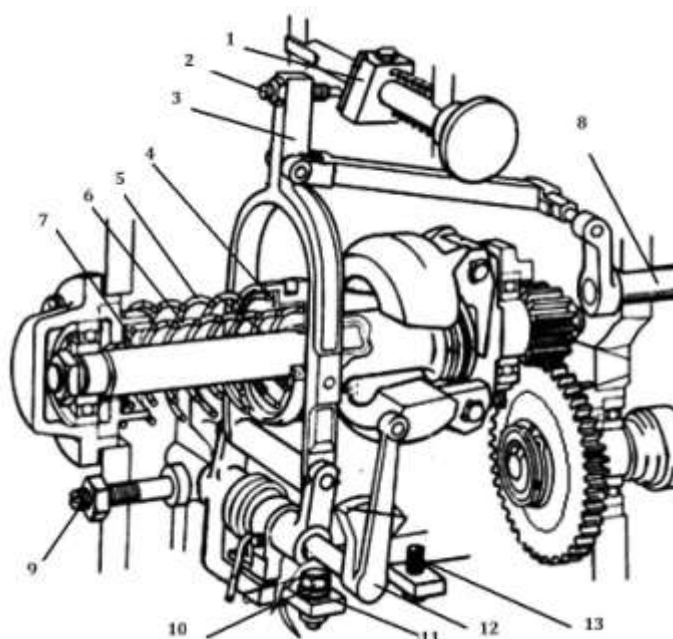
Регулятор ТНВД серии ТН: 1 - призма; 2 - болт номинала; регулировочные шайбы; 3 - основной рычаг; 4, 7, 11 - регулировочная шайба; 5, 6 - пружина регулятора; 8 - рейка топливного насоса; 9 - болт-ограничитель; 10 - болт максимального скоростного режима; 12 - рычаг управления регулятором; 13 - винт останова.
